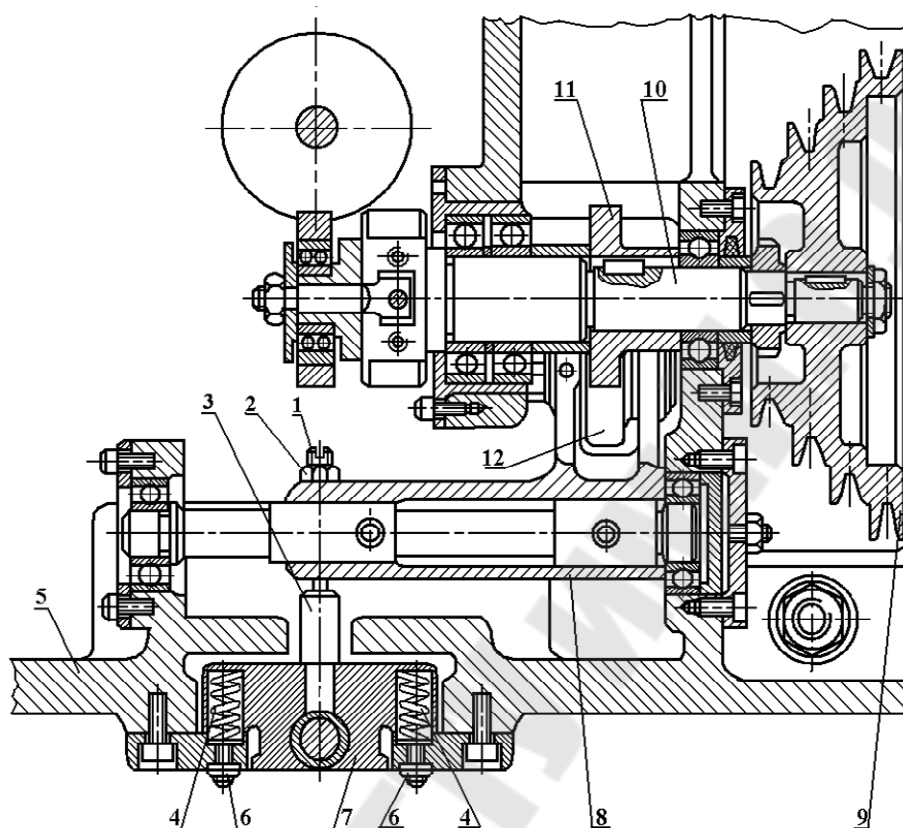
Эскиз механизма отвода долбяка от заготовки
